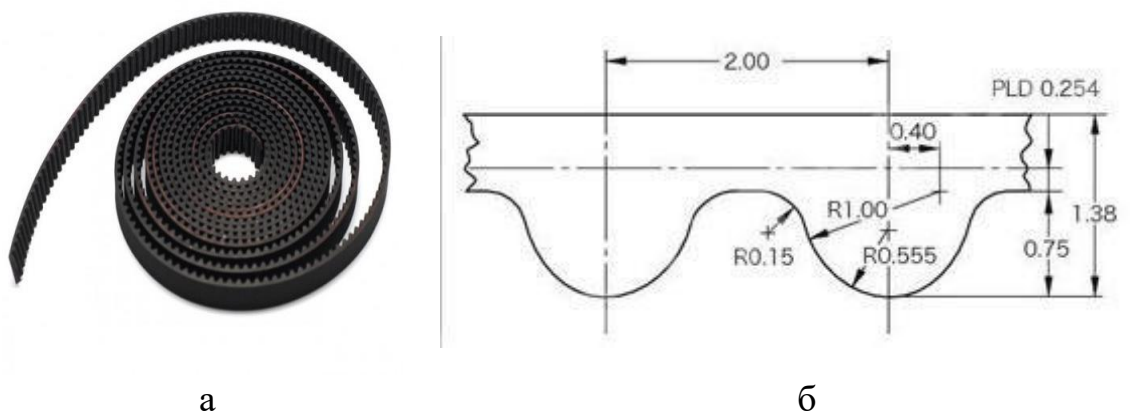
Зубчастий пас GT2-6: а – загальний вигляд; б – розміри профіля [12]
